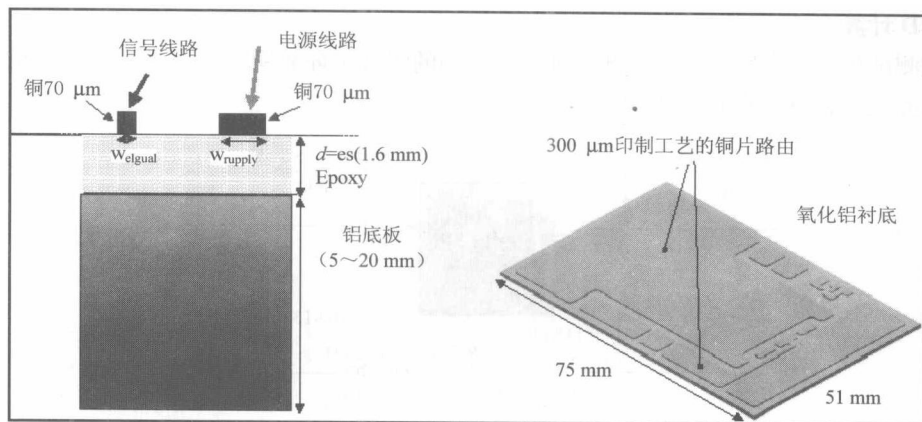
功率 PCB（2D 视图）和 300 μm 铜和氮化铝的夹层（3D 视图）
